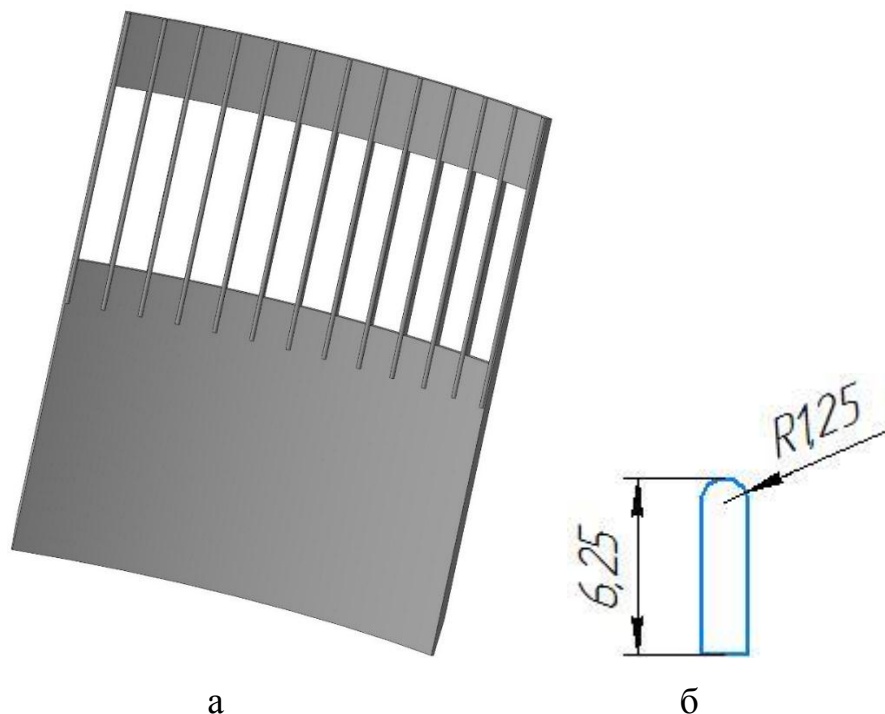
Модель робочого органа: а – загальний вигляд робочого органа; б – геометричний переріз прутка
